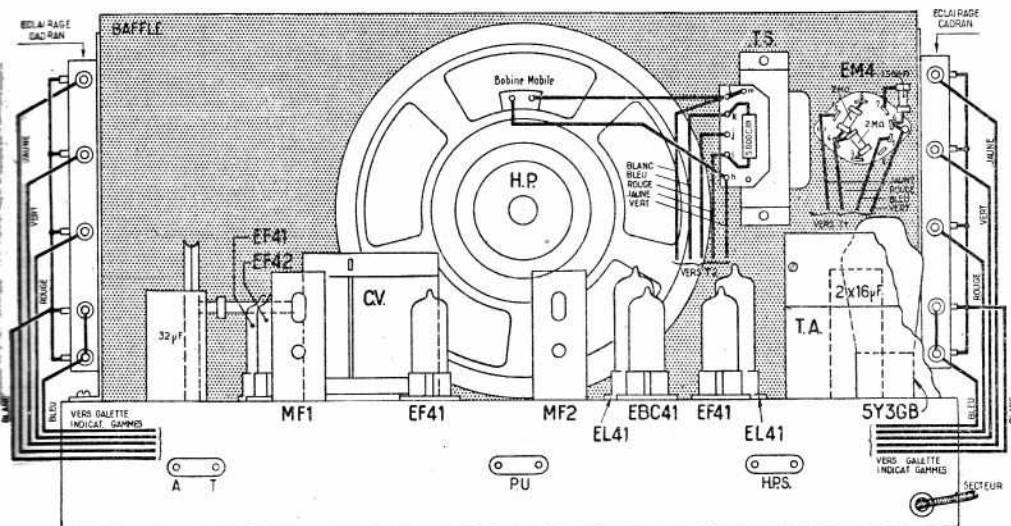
VUE ARRIÈRE DU RÉCEPTEUR
